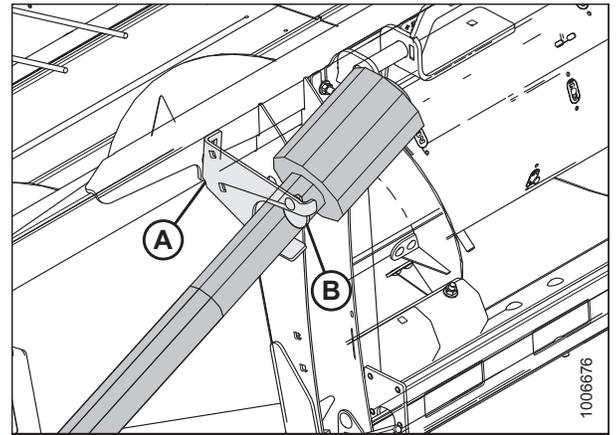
Extremo de la cosechadora del cardán en posición de almacenamiento
